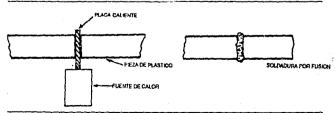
Soldadura por fusion. (Ref. 2).
